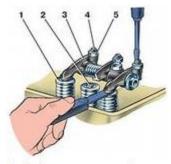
1- тарелка пружины, 2 шпиндель клапна, 3 - коромысло, 4 - регулировочный винт, 5 контрогайка
